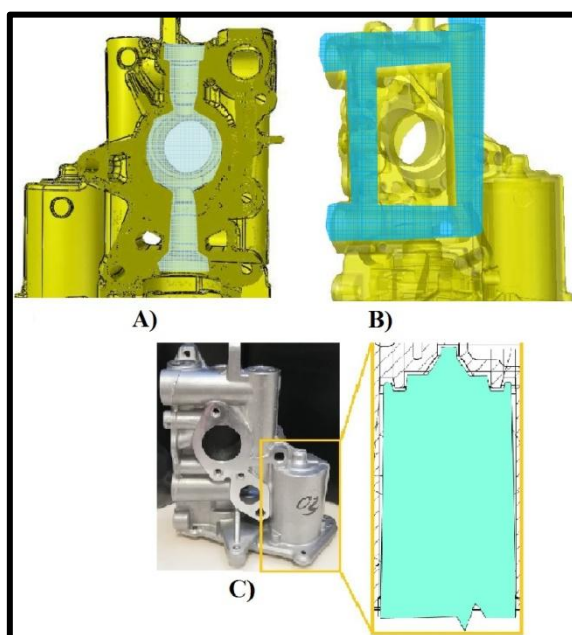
OM654 EGR ventil - verze s označením 329 [3]
